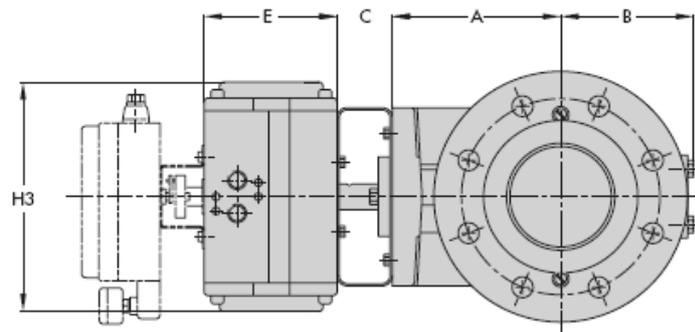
• Габаритные размеры Тип 3310 / BR 31a
